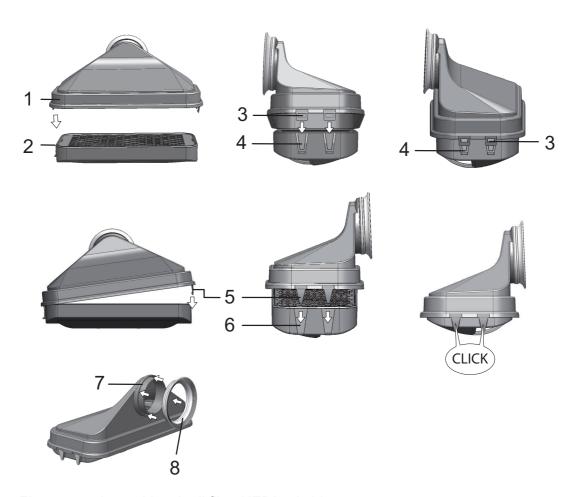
Assemblaggio di filtro HEPA ed airbox
